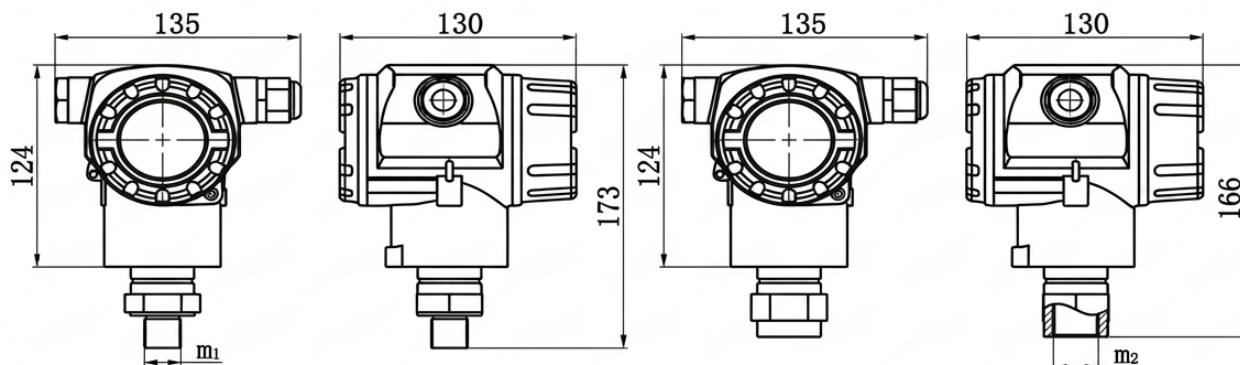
Габаритные размеры резьбового исполнения (мм)
